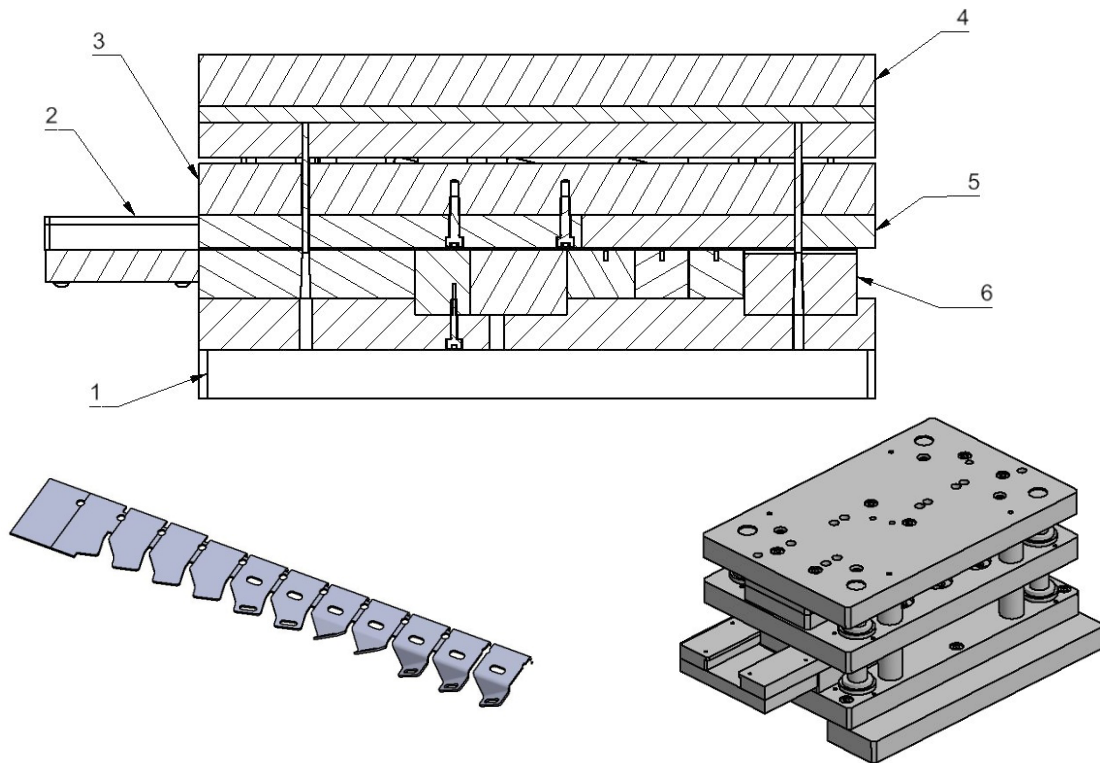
Folgeverbund Stanz-Biegewerkzeug
